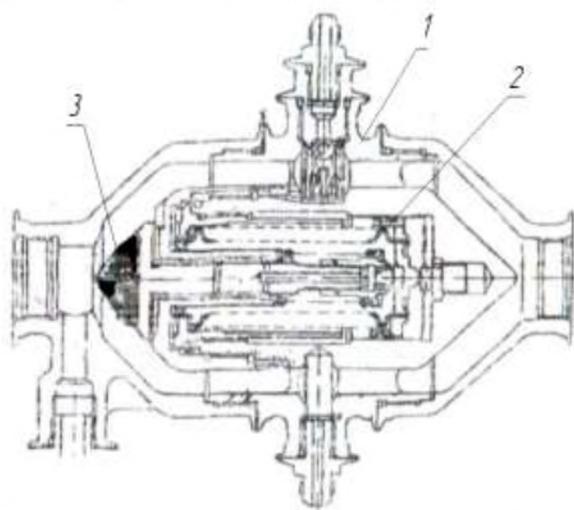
Клапан перекрывной (1 - корпус; 2 - сильфонный привод; 3- уплотнительный элемент)
